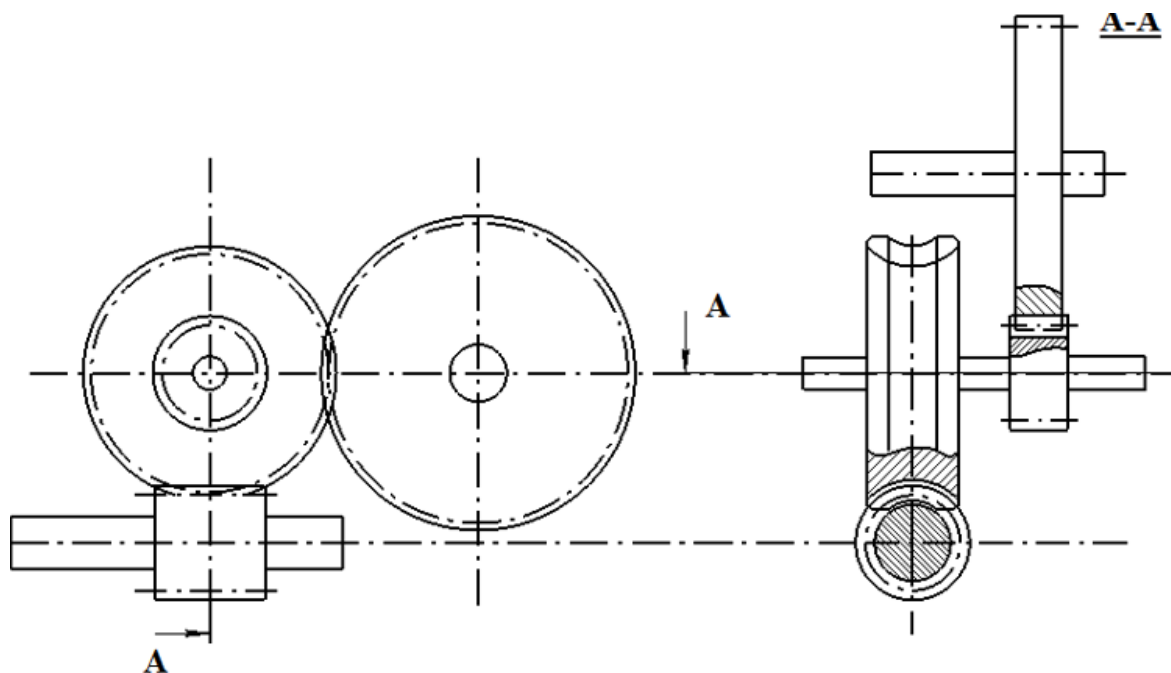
Схема расположения ступеней двухступенчатого червячно-цилиндрического редуктора
